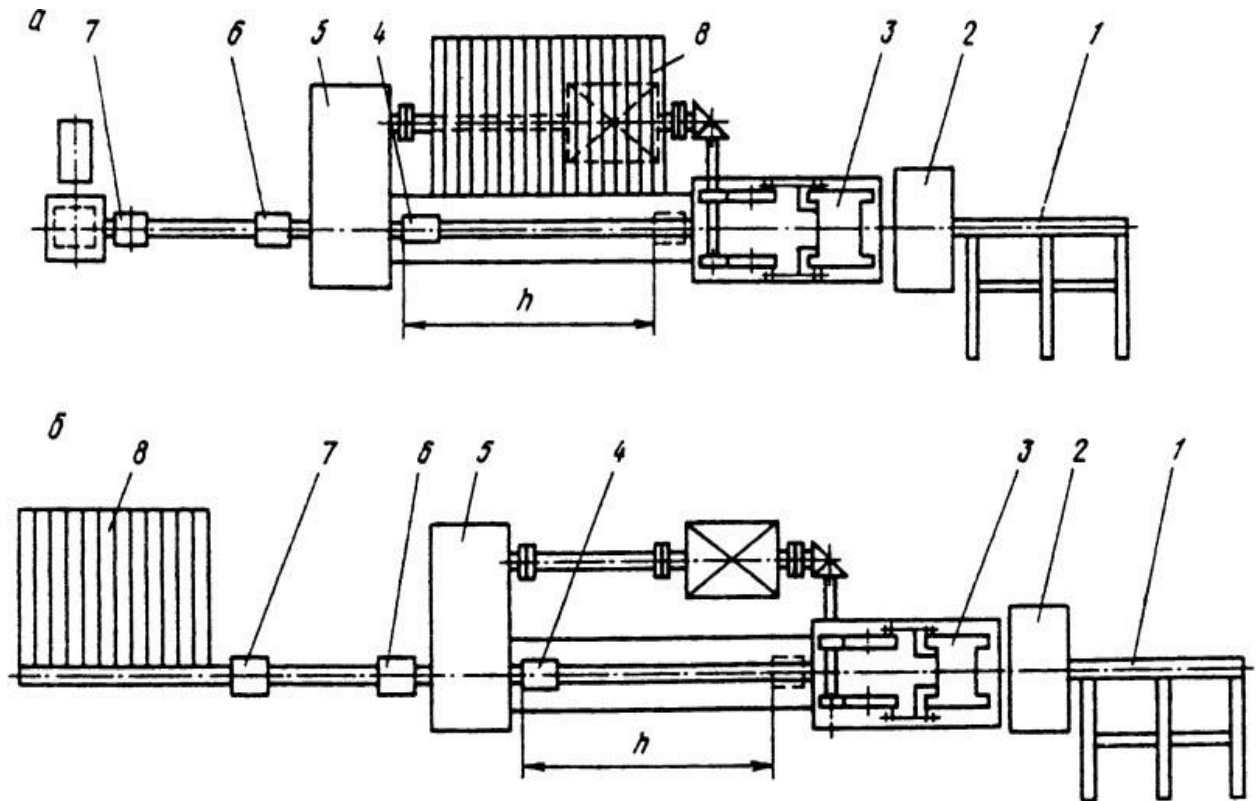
Схеми розташування устаткування станів холодної прокатки труб з бічним (а) і торцевим (б) завантаженням заготовок: 1 – готова труба; 2 – летуча пила; 3 – робоча кліть; 4 – патрон заготовки; 5 – привід патрону стрижня оправки; 6 – патрон стрижня; 7 – відкритий затискач стрижня; 8 – приймальний стіл
